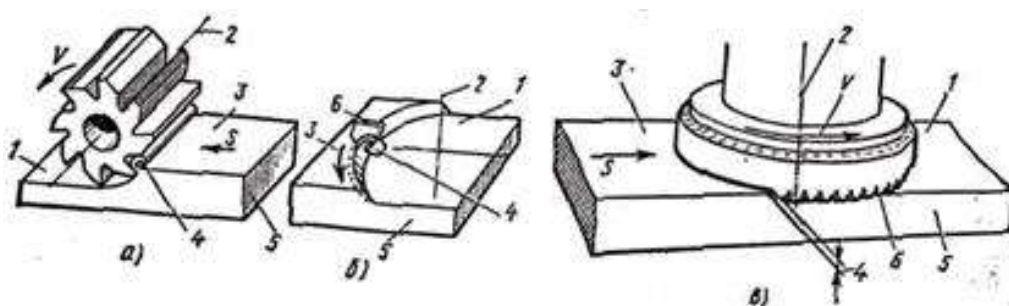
Схемы фрезерования: а — цилиндрическое, б и в — торцовое фрезерование; 1—обработанная поверхность, 2-ось вращения фрезы, 3 — обрабатываемая поверхность, 4— стружка, 5 — заготовка, 6 — нож фрезы.
